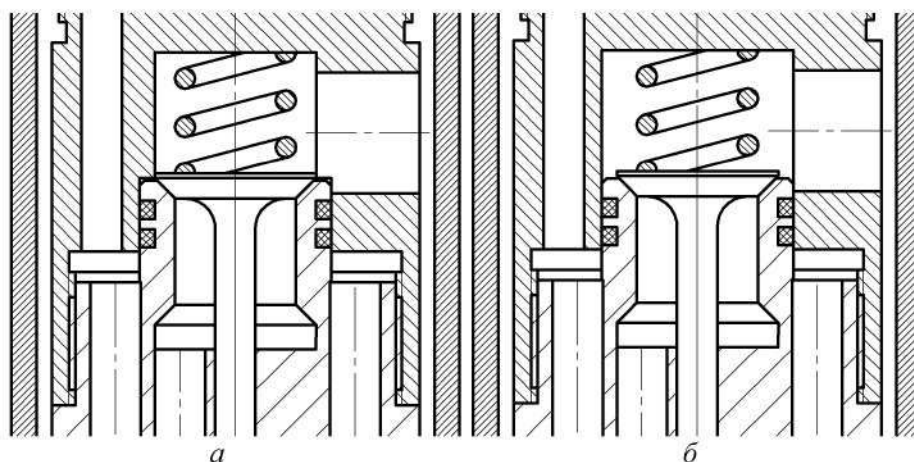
Расположение впускного клапана в клапанной коробке гидроударника: а – исходная конструкция; б – конструкция со сниженными гидравлическими сопротивлениями
